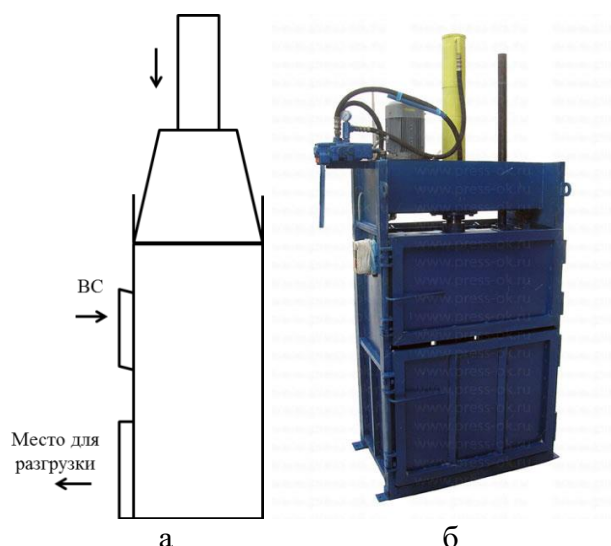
Вертикальный пресс: а – схема пресса; б – общий вид
